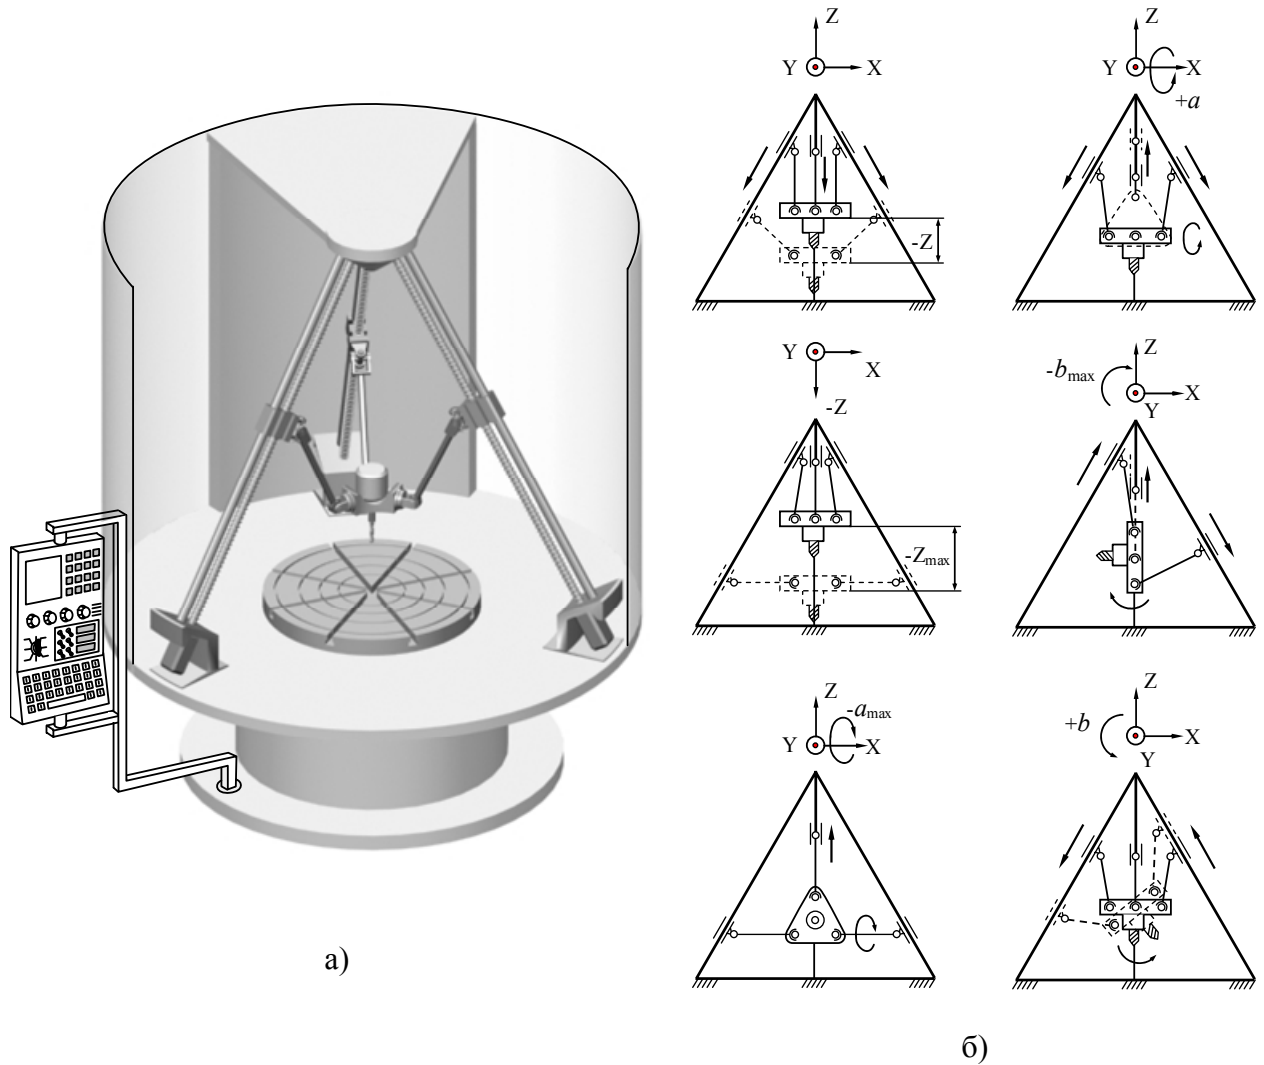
Багатокоординатний свердильно-фрезерний верстат підвищеної жорсткості:
